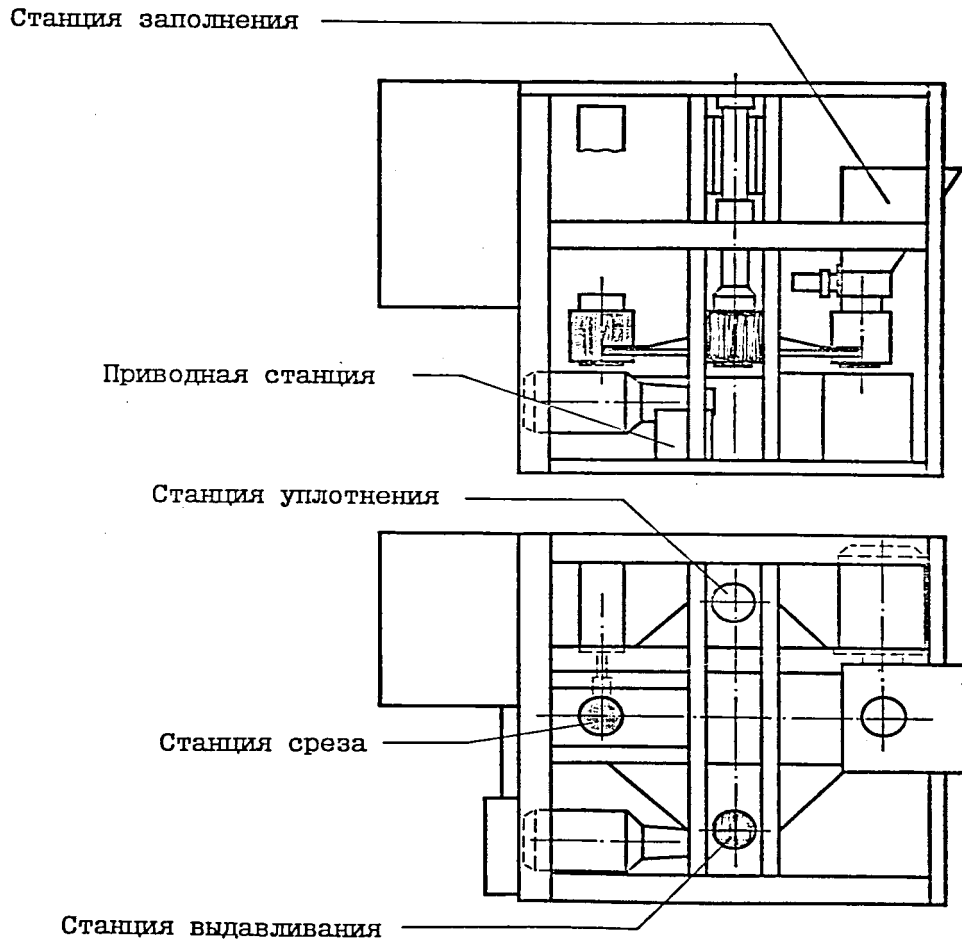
Типовая компоновочная схема устройств для автоматического контроля свойств формовочных смесей
